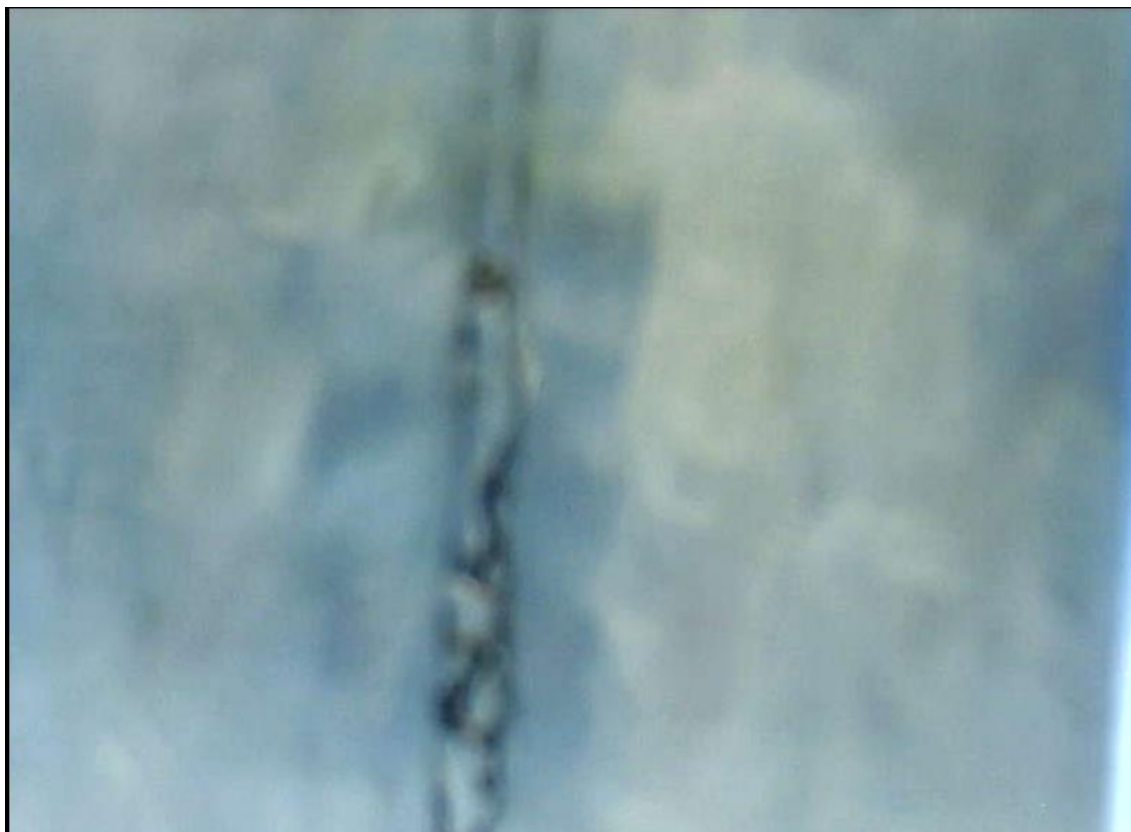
Defectos en soldadura observados a través del ROV en el agua.
